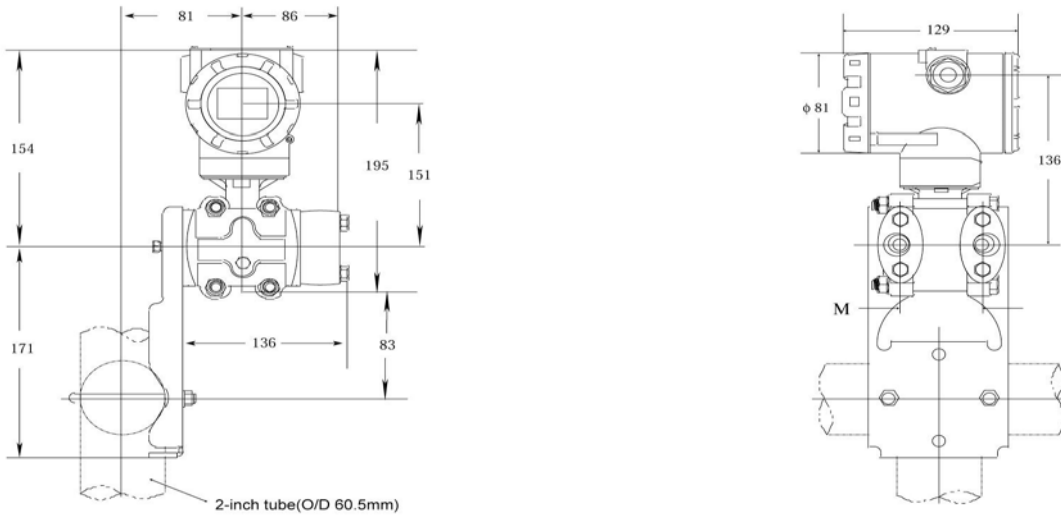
Внешний вид и размеры фланца датчика CDS-3151M LT
